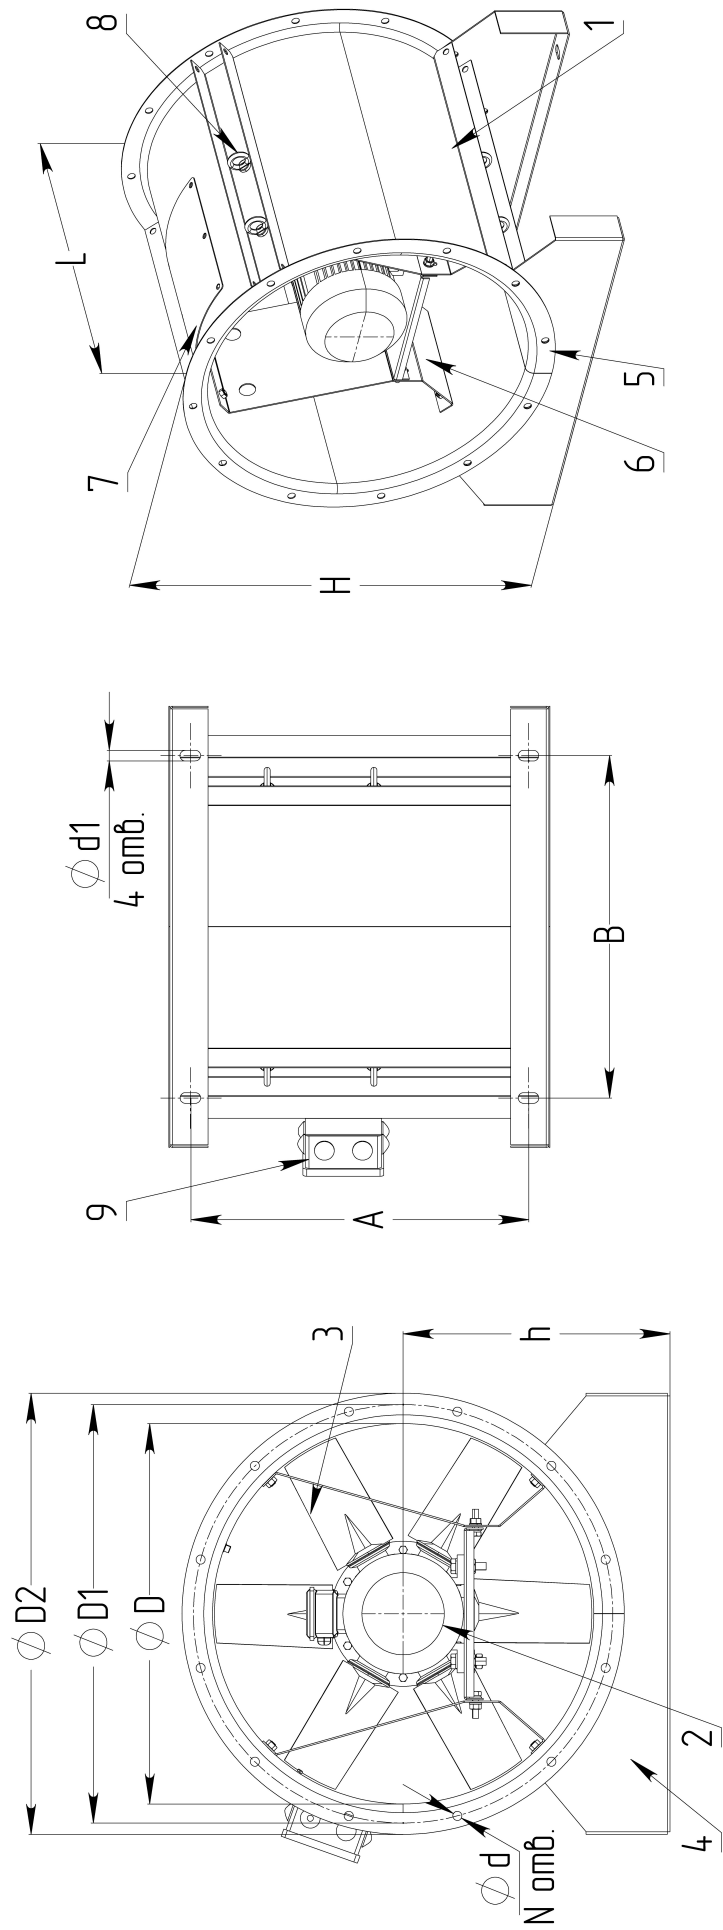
Вариант исполнения вентилятора на горизонтальной опоре
